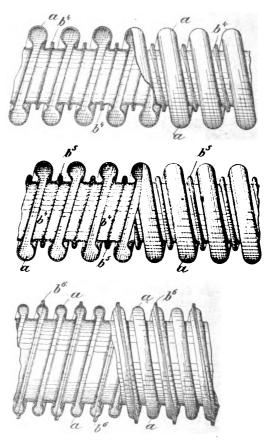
Geschweißter Schlauch, schraubenförmig gewickelt.
